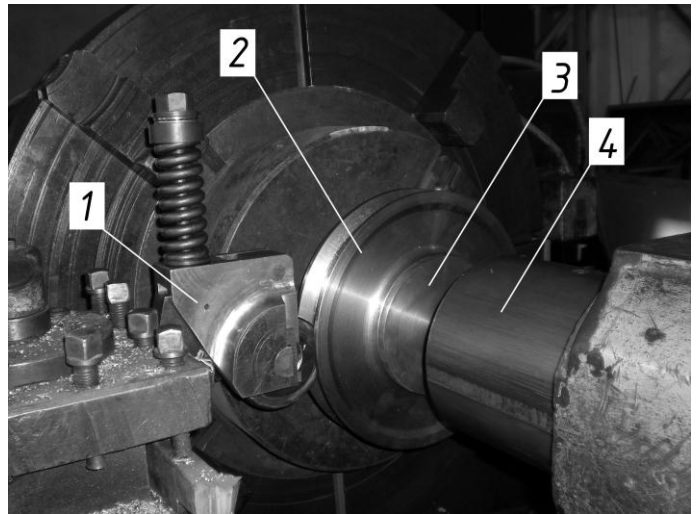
Общий вид экспериментального оборудования: 1 – устройство для обкатывания канатных блоков; 2 – канатный блок; 3 – оправка; 4 – задняя бабка токарного станка
